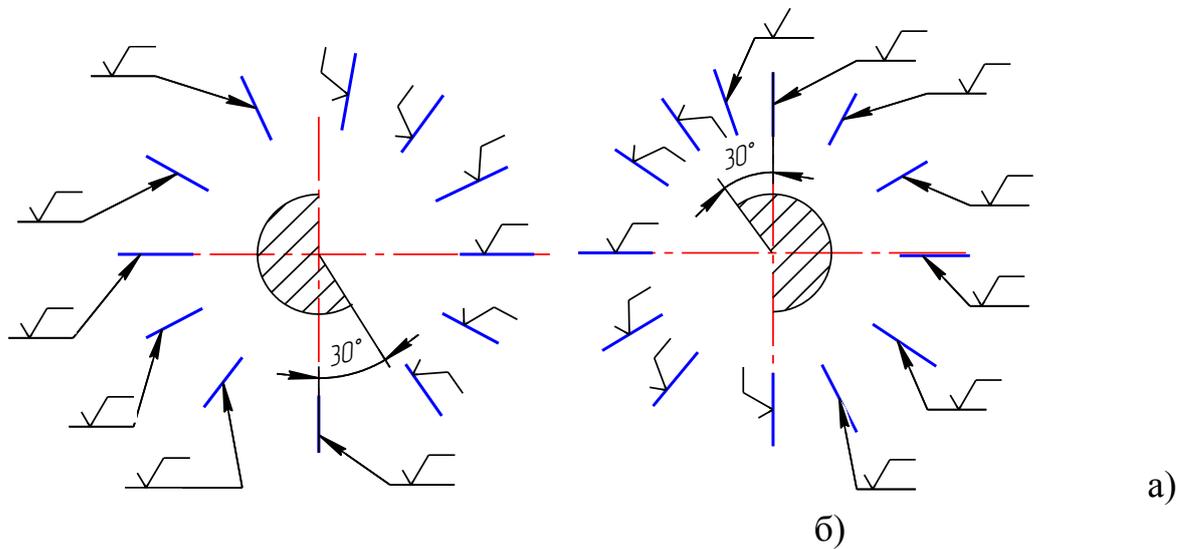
Расположение знака обозначения шероховатости с полкой, относительно основной надписи чертежа [21]
